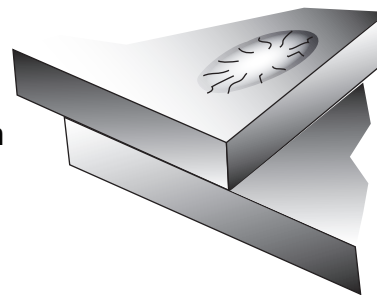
Joint typique pour le soudage à l'arc
